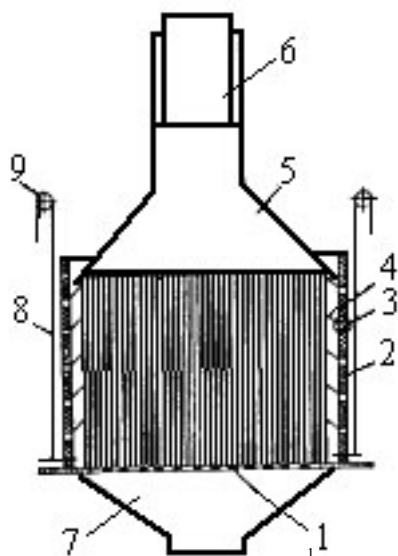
Установка для сушки паковок (авт. свид. SU №1486719)
